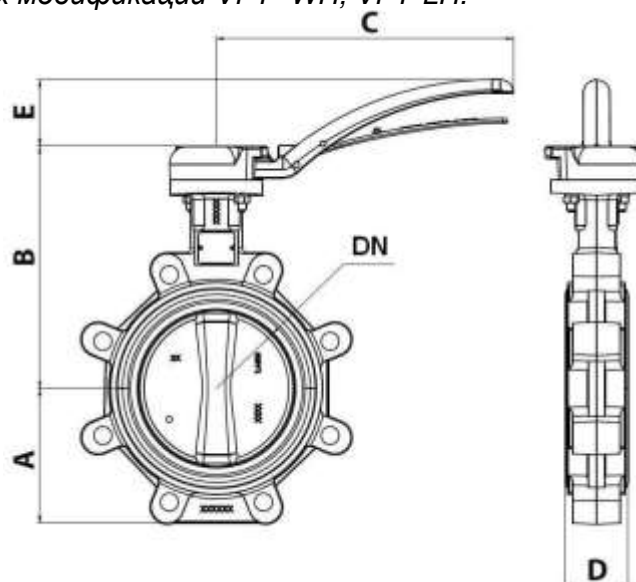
Габаритные и присоединительные размеры затворов дисковых поворотных модификации VFY- LH с резьбовыми отверстиями под болты
